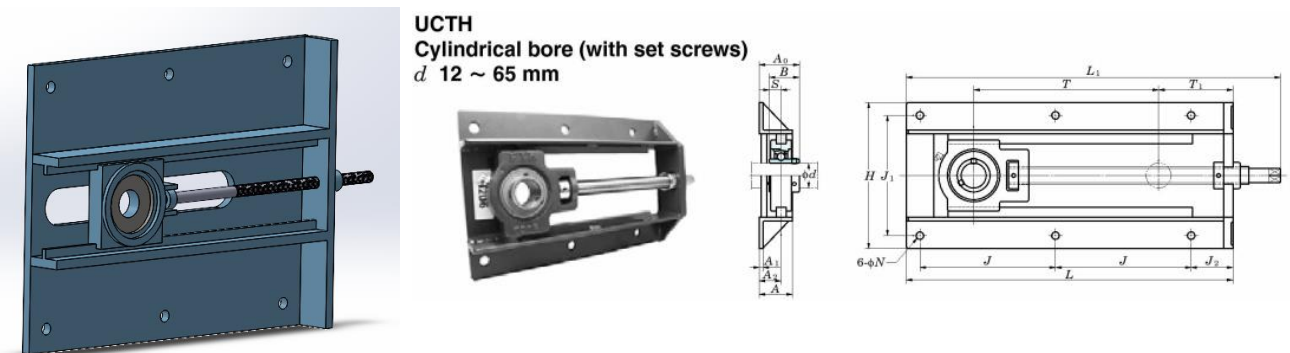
Conjunto tensor – Rodamiento + Tornillo + Bastidor
